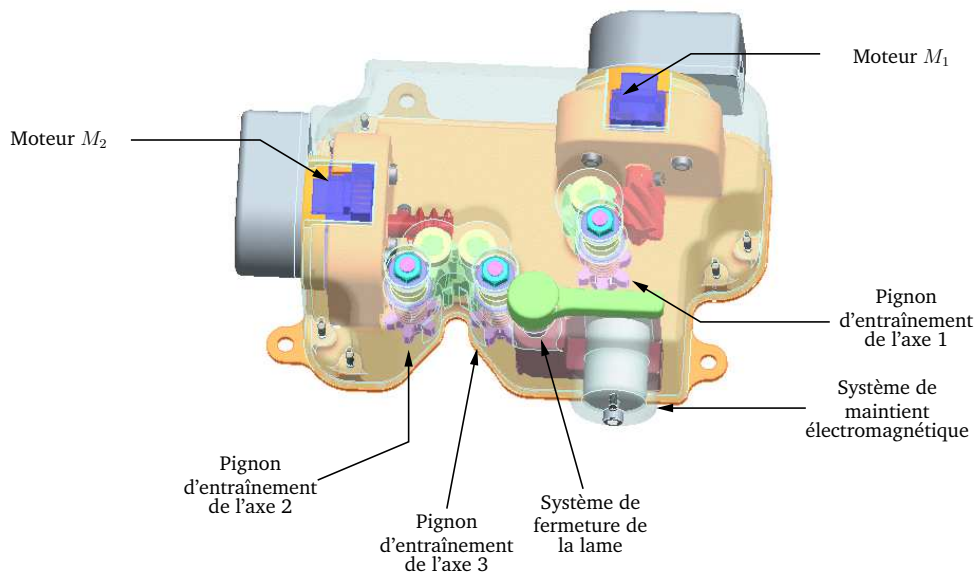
Vue CAO du mécanisme d'entraînement motorisé.
